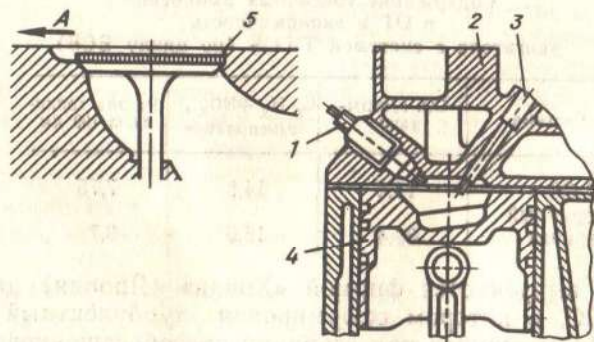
Схема двигателя с FCP-процессом; 1 — свеча зажигания; 2 — головка цилиндра; 3 — форсунка; 4 — поршень; 5 — ширма клапана; А — направление воздушного вихря
